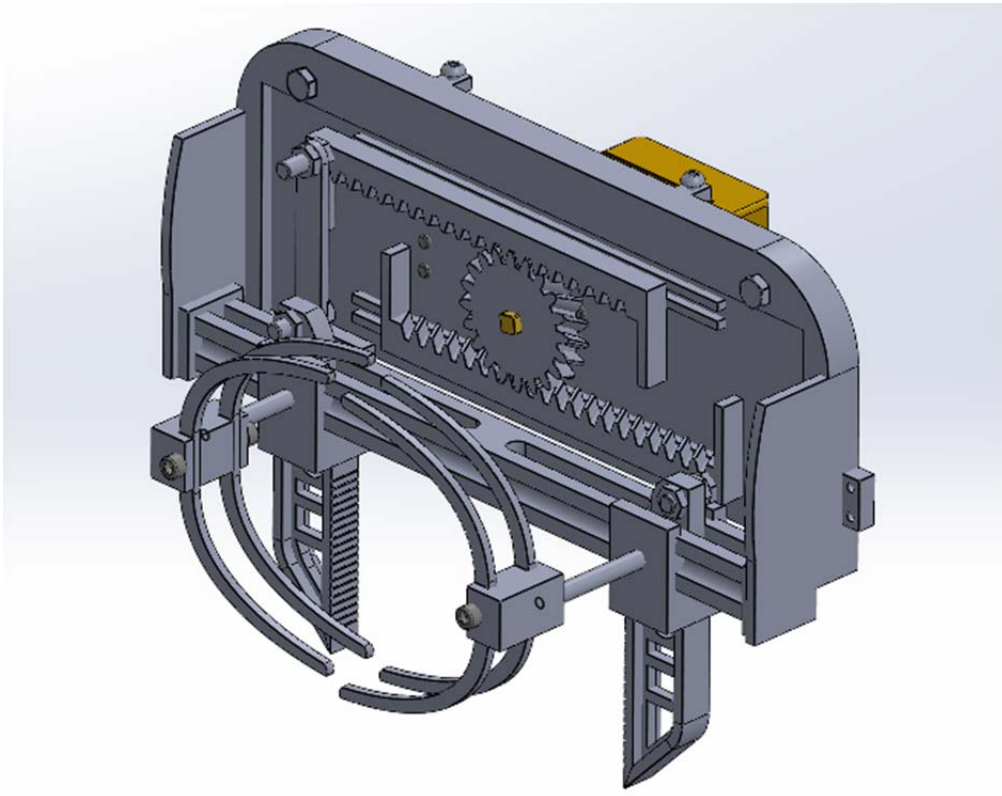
Mecanismos herramienta robótica definitivo (vista isométrica, en apertura)
